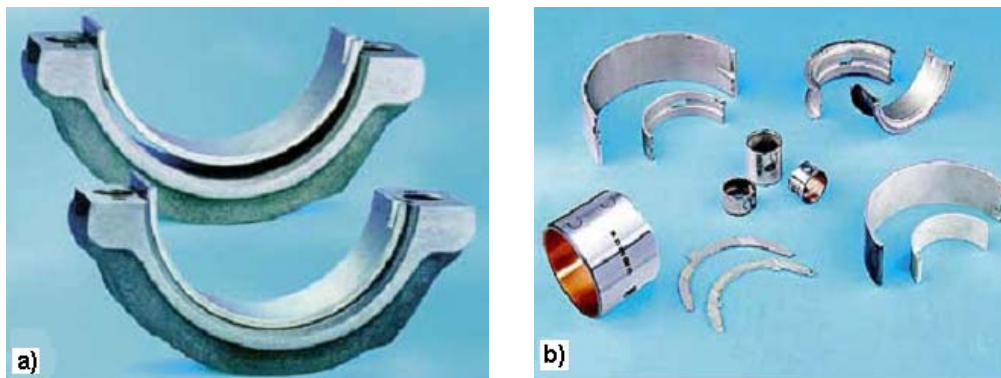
a) Cojinetes para bielas b) Cojinetes y bujes de un motor de combustión interna.[2]
